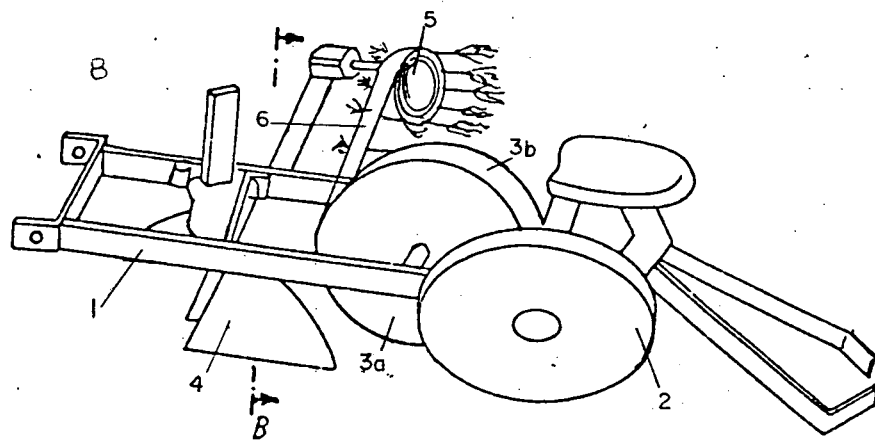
Vista da montagem do dispositivo |7|.
